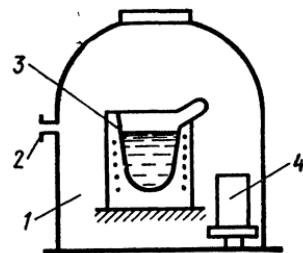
Установка для вакуумной плавки и заливки стали в литейную форму:
